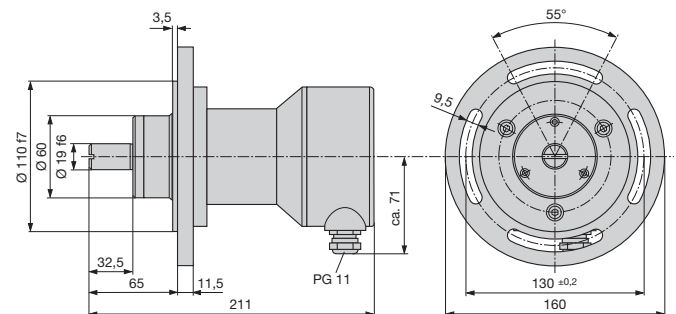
KINAX WT717 с дополнительным редуктором и фланцем.
